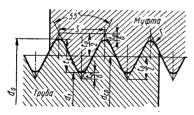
Профиль трубной цилиндрической резьбы по ГОСТу $6357-52; t_0=0.96049 \ S;$ $t_2=0.64031 \ S; \ r=0.13733 \ S$
